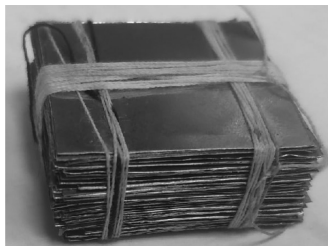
Заготовка перед диффузионной сваркой
